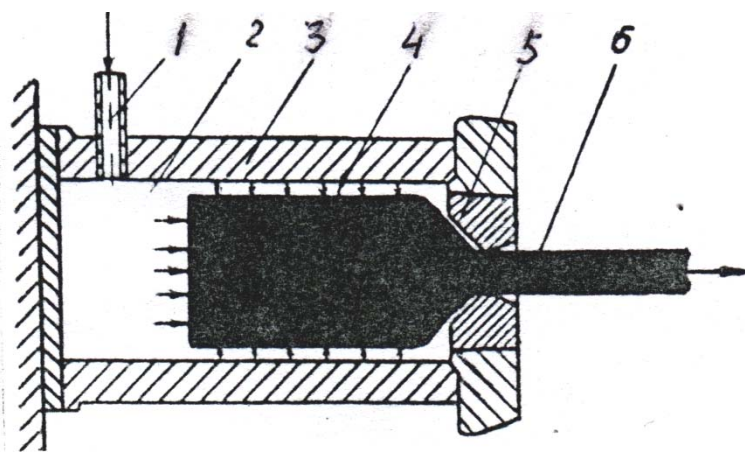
Принципова схема процесу гідропресування: 1 - підведення робочої рідини в контейнер; 2 - робоча рідина; 3 - контейнер; 4 - заготовка; 5 - матриця; 6 - прес-виріб
